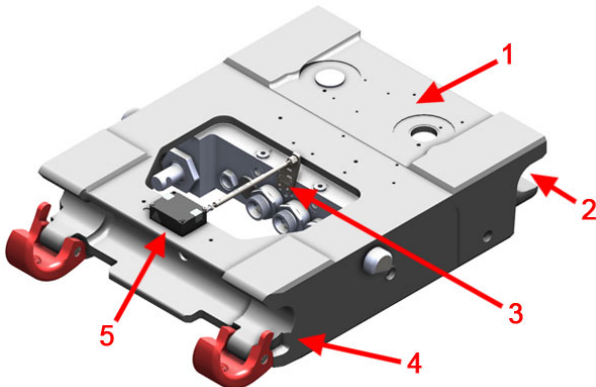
Chassis mit hydraulischen Verriegelungskomponenten
